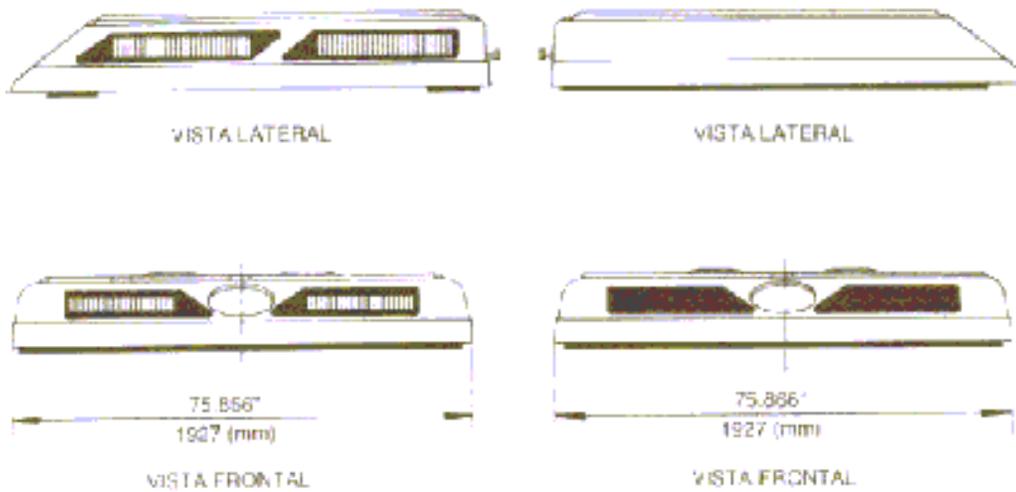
DIMENSIONES LATERALES DE EQUIPO WIDE UNIT⁴⁶
